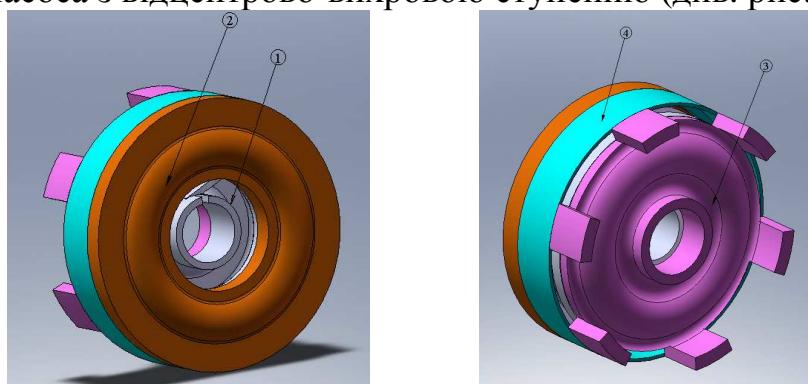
Загальний вид ступені: 1 – РК; 2 - передня вихрова ступень; 3 - задня вихрова ступень; 4 – корпус РК.
